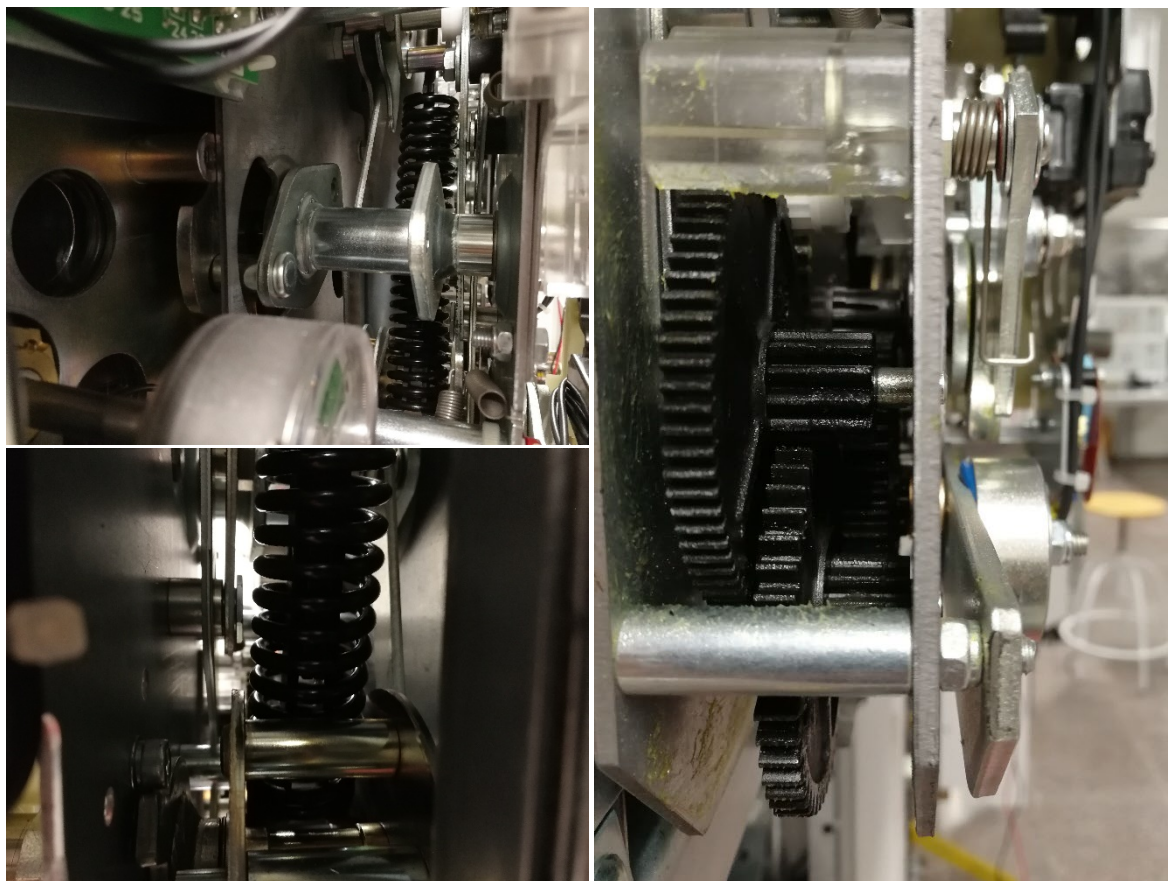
Detalles del mecanismo de accionamiento.
